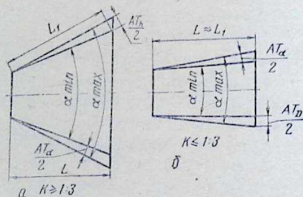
Допуски угловых размеров и их обозначения.
